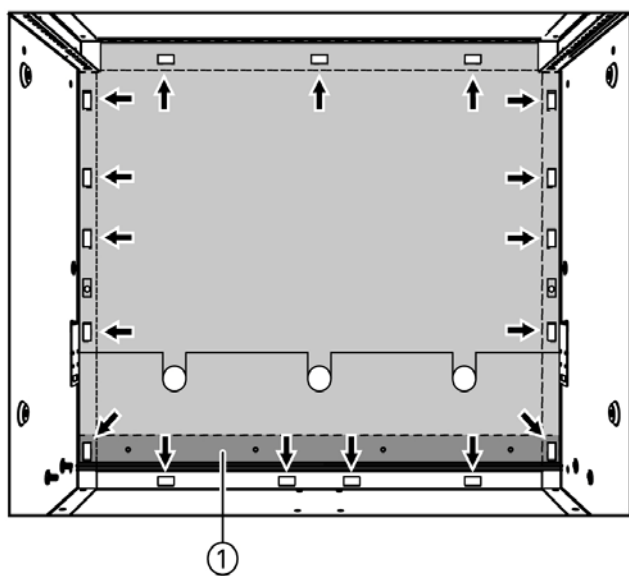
Точки крепления для ячеек с прокладкой кабеля
